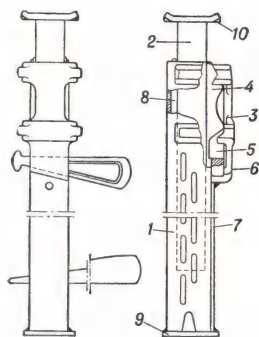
Клиновидная металлическая стойка: 1 — корпус; 2 — выдвижная часть; 3 — клиновидный замок; 4 — рабочий клин; 5 — передаточный клин; 6 — горизонтальный клин; 7, 8 — планки; 9 — нижняя опорная плита; 10 — верхняя опора.
